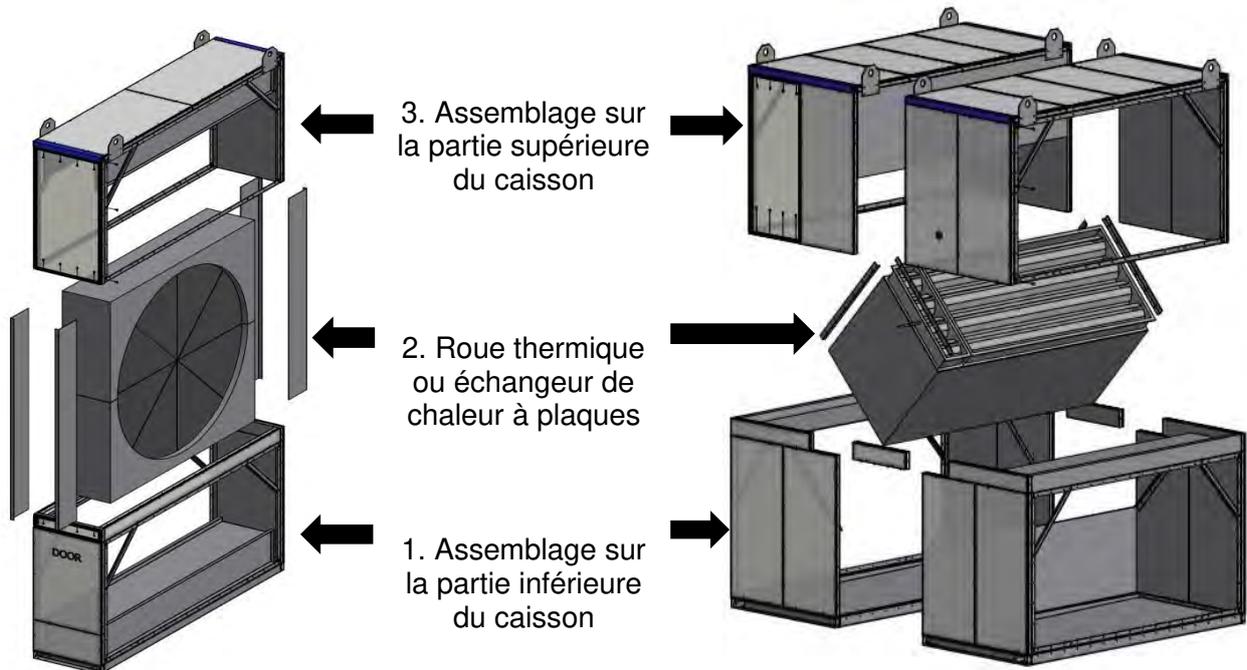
Ordre de montage de la roue thermique démontée ou de la section de caisson d'échangeur de chaleur à plaques
